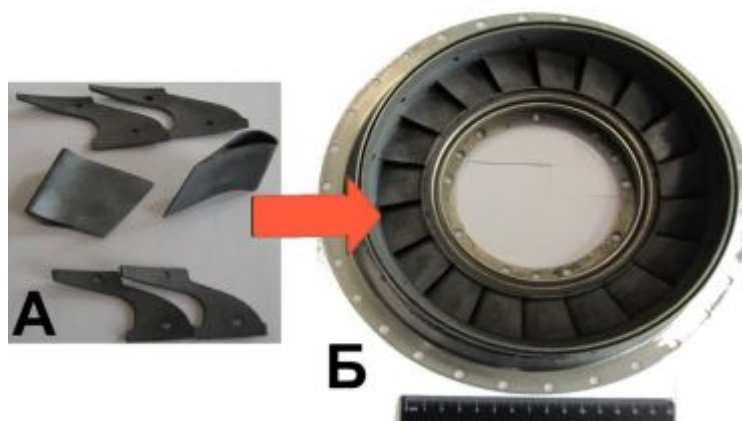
Разработанный и изготовленный СА исходной конструкции из ККМ
